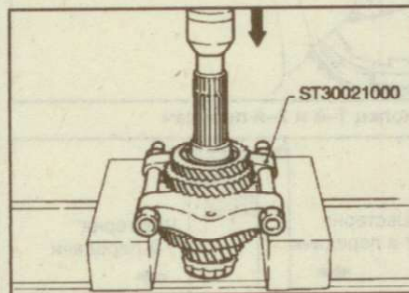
Выпрессовка вторичного вала с шестерни 3-й передачи и шестерни 2-й передачи
